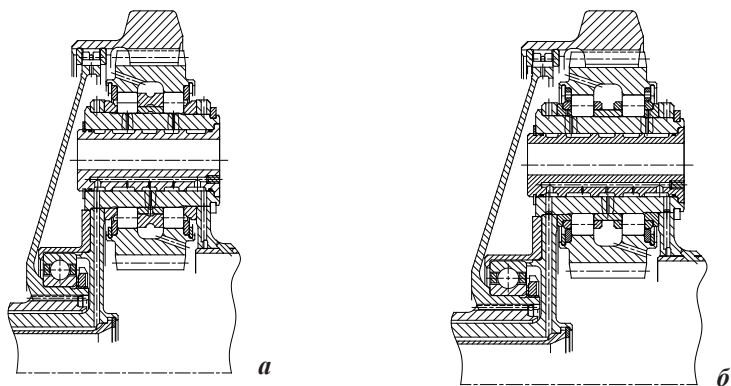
Схема подвода смазки в подшипники главного редуктора двигателя ТВЗ-117ВМА-СБМ1:
